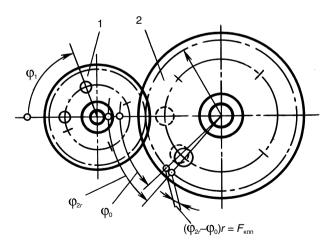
Схема определения кинематической погрешности зубчатой передачи
